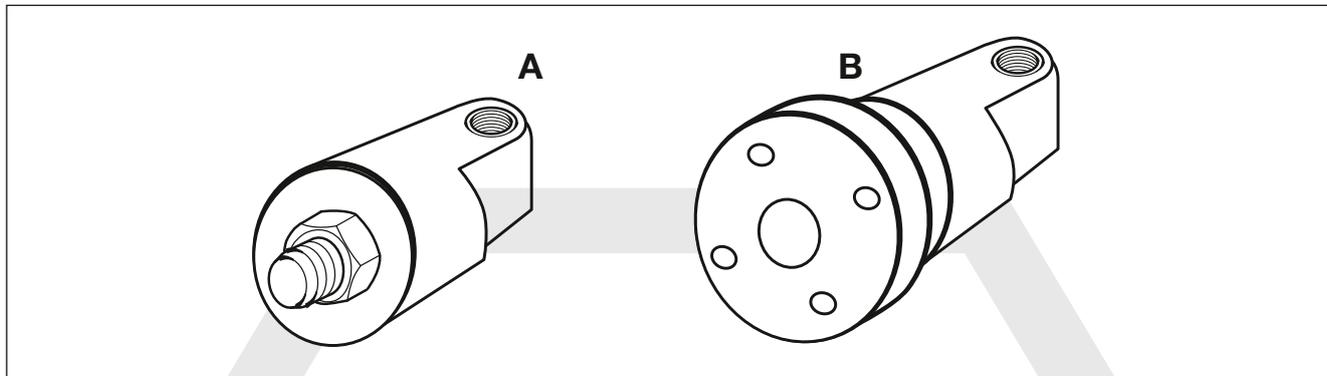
Varianten für die Befestigung an die Maschinenwelle
